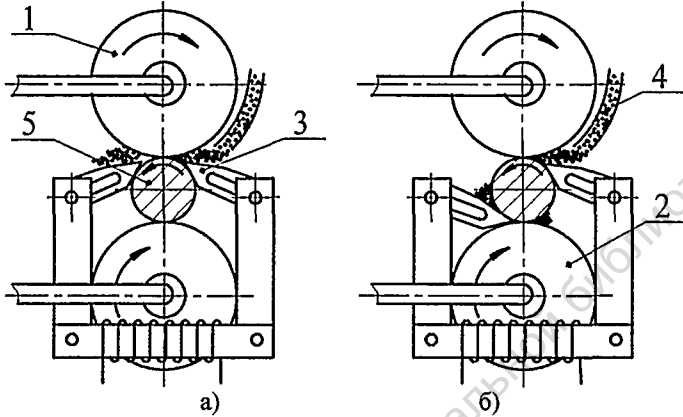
Схемы способов установки полюсов электромагнита и подачи порошка в зоны приварки: а) первая схема – подача в верхнюю зону приварки; б) вторая схема приварки – подача в верхнюю и нижнюю зоны приварки: 1,2 – электроды; 3 – полюс ЭМ; 4 – порошокпровод; 5 – восстанавливаемая деталь.
